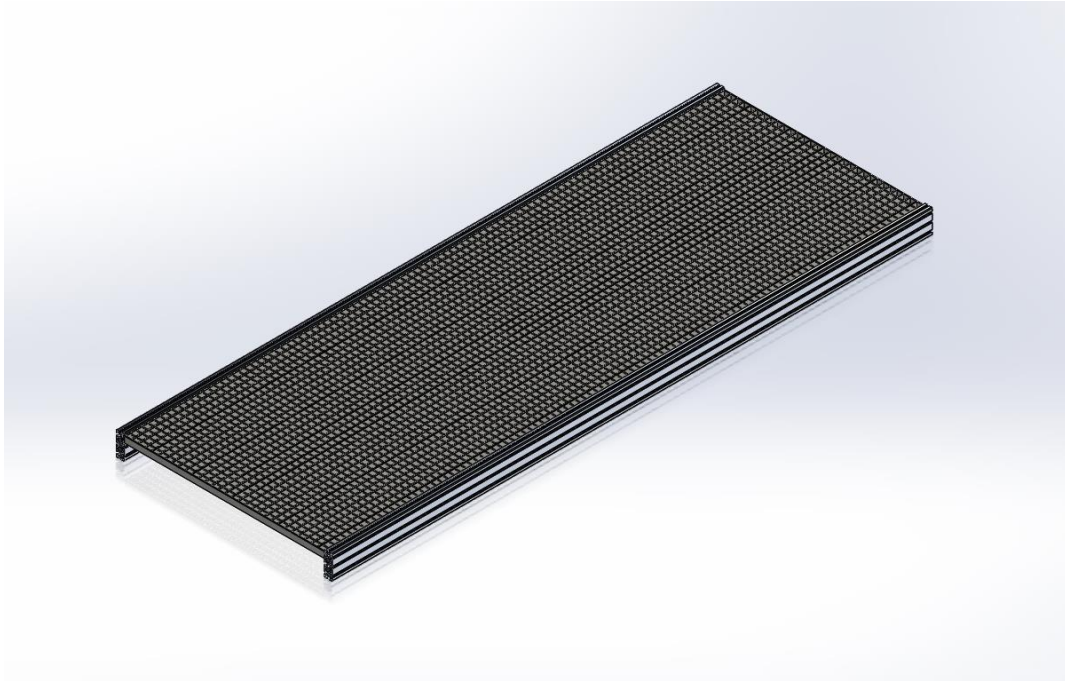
Piso, emparrillado electrosoldado de galvanizado.
